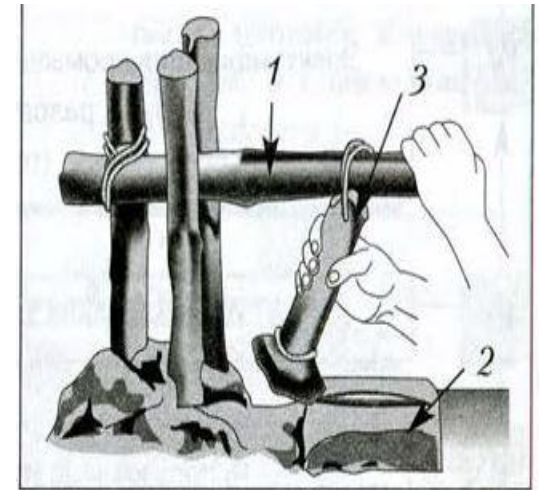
Древнее приспособление для резки камня: 1 — нажимной рычаг; 2 — заготовка; 3 — оправка (совершает качательное возвратно-поступательное движение)
